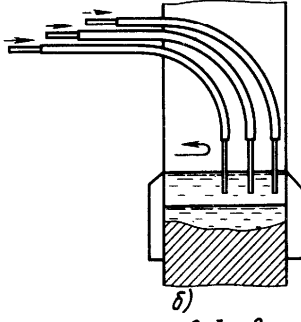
Схема процесса электрошлаковой сварки
